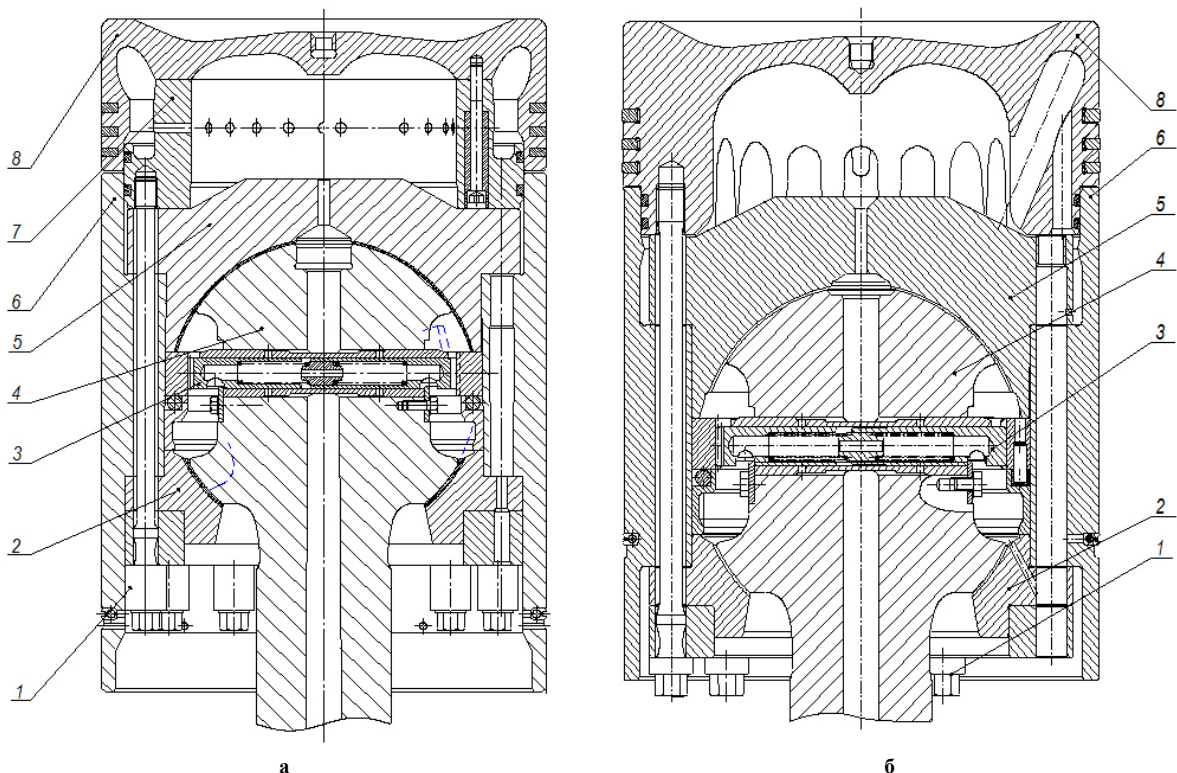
Поршні двигунів: а – Sulzer ZL40; б – ZA40S 1 – гвинт; 2, 5 – нижній та верхній шарнірні вкладиші; 3 – храповий механізм; 4 – шарнірна головка шатуна; 6 – юбка поршня; 7 – охолоджувальний вкладиш; 8 – головка поршня
